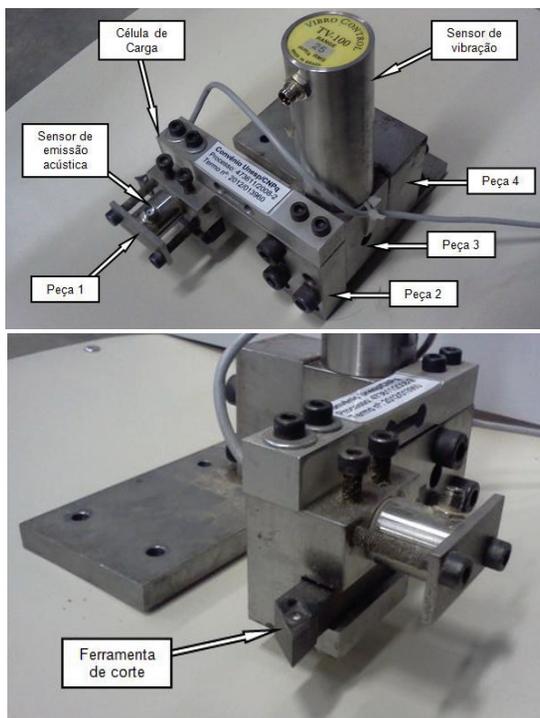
Dispositivo projetado e montado com sensores e ferramenta de corte.
